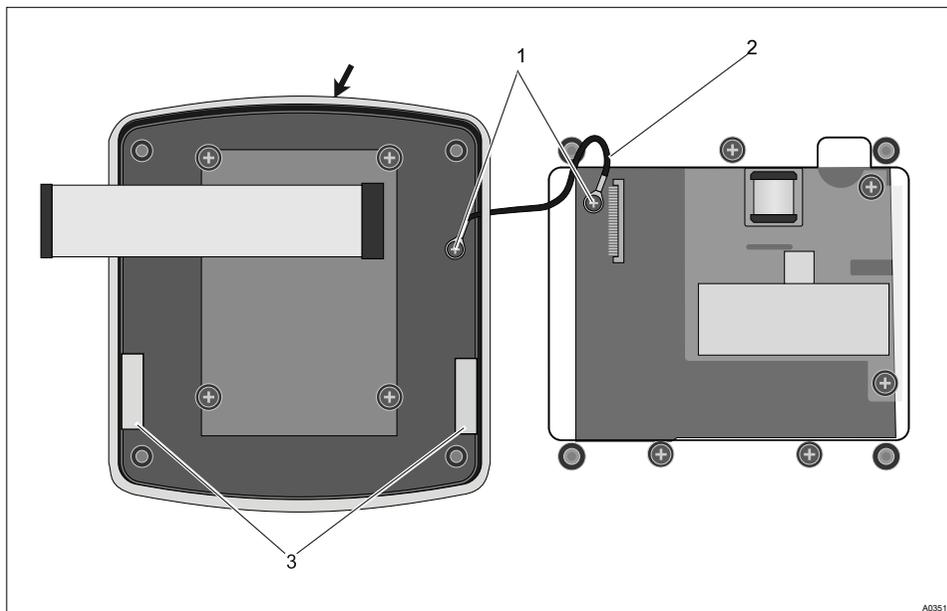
Установка профильного уплотнения на верхней части корпуса регулятора
